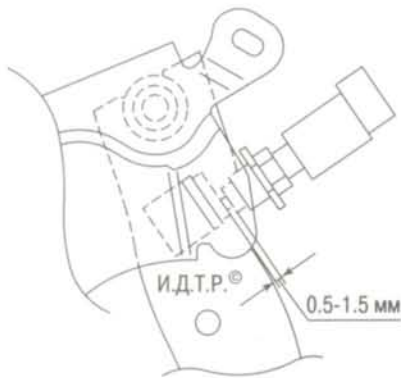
Регулировка зазора датчика выключения сцепления
